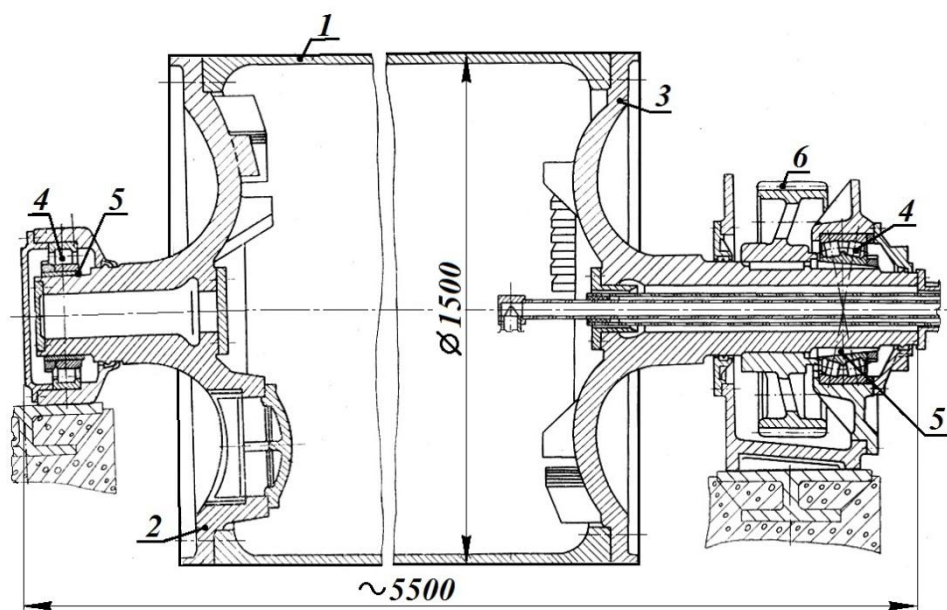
Сушильный цилиндр: 1 – цилиндр; 2 – крышка-цапфа лицевой стороны; 3 – крышка-цапфа приводной стороны; 4 – подшипник качения; 5 – разжимная втулка; 6 – шестерня
